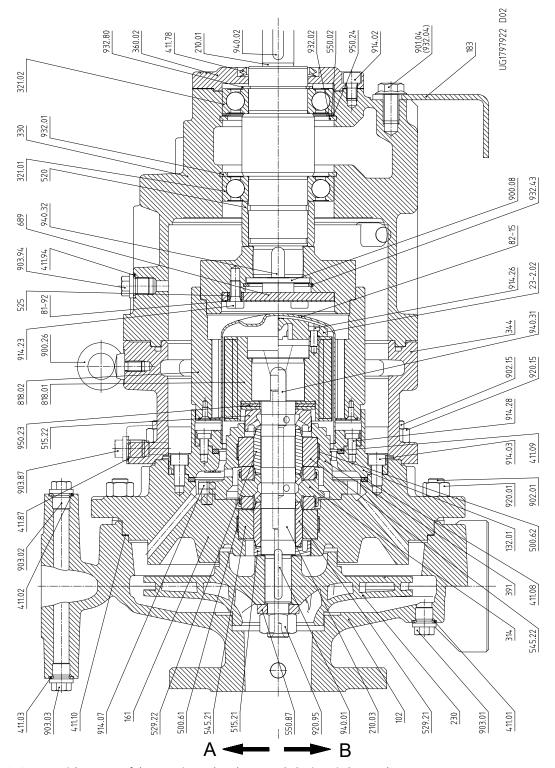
Gesamtzeichnung Ausführung mit geschraubtem Deckel mit Zwischenstück
